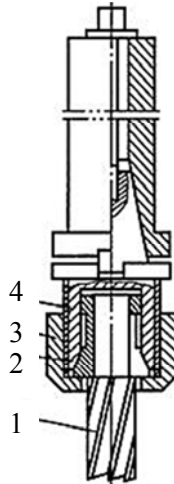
Установка концевых фрез с цилиндрическим хвостовиком в цанговом патроне: 1 – фреза; 2 – цанга; 3 – гайка; 4 – патрон
